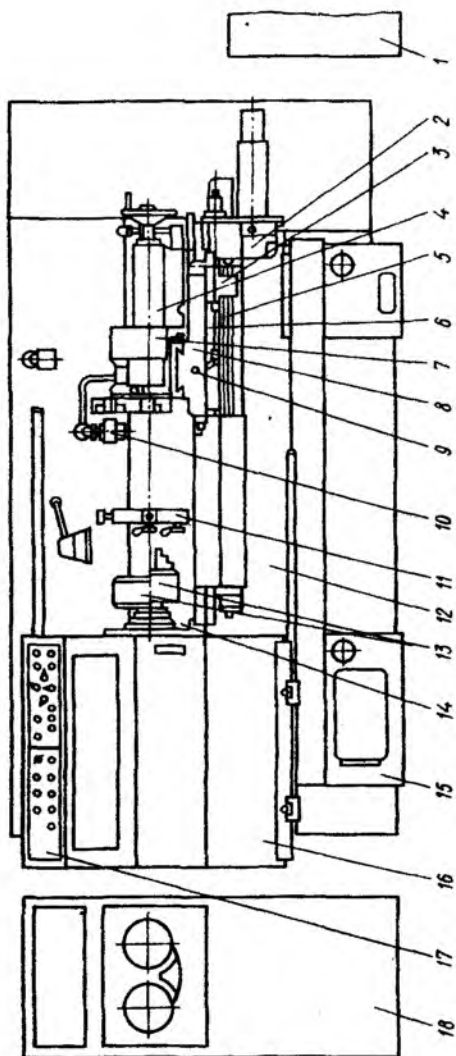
Общий вид токарного станка с ЧПУ мод. 16К20Ф3
